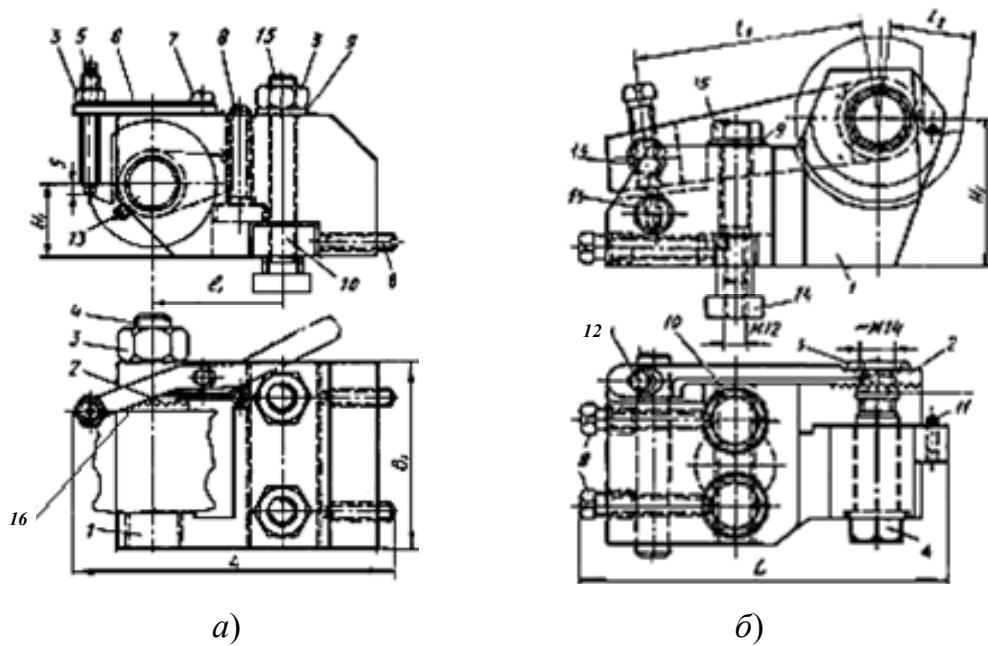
Эскизы державок для крепления дисковых резцовых головок на суппорте станка:
